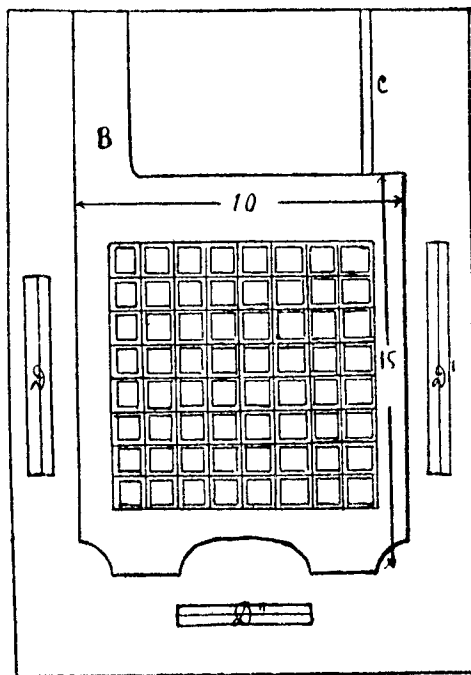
Вид гипсовой формы для отливки аккумуляторных пластин.
